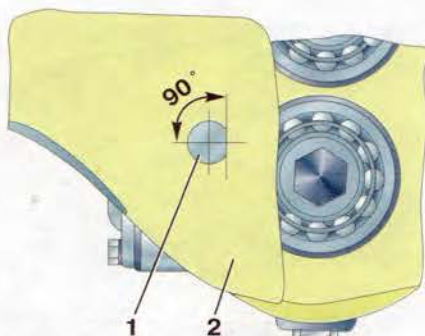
Установка оси промежуточной шестерни заднего хода: 1 – ось; 2 – пластина
